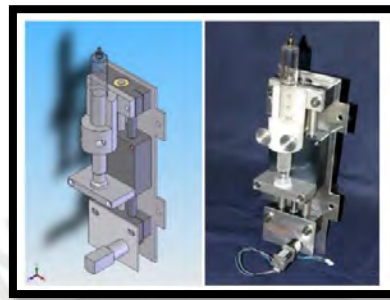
Diseño y construcción de la bomba de inyección.
